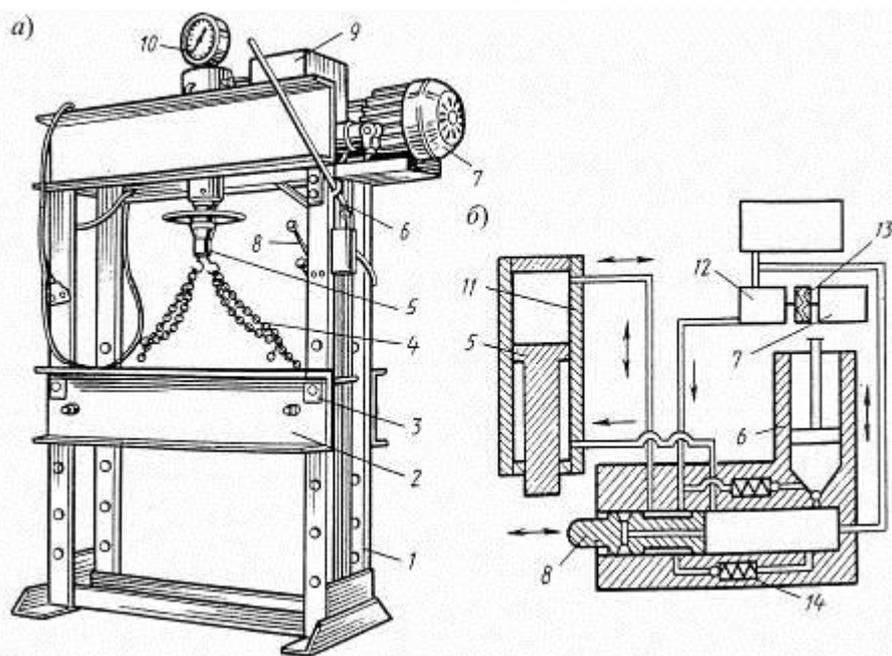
Стационарный гидравлический пресс ОКС-1671М: а — общий вид; б — гидравлическая схема; 1 — рама; 2 — станина; 3 — палец; 4 — цепи; 5 — шток; 6 — ручной насос; 7 — электродвигатель; 8 — золотник; 9 — бачок рабочей жидкости; 10 — манометр; 11 — гидроцилиндр; 12 — гидронасос; 13 — муфта; 14 — предохранительный клапан
